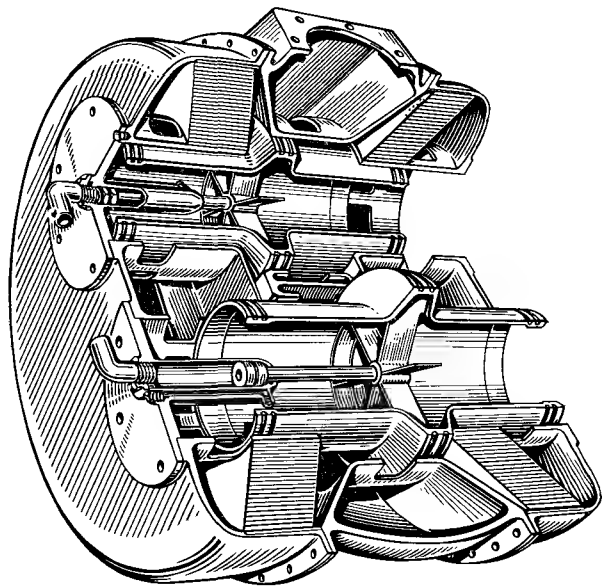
Регенеративный подогреватель фирмы Парсонс с неподвижной матрицей и пневматическим приводом
